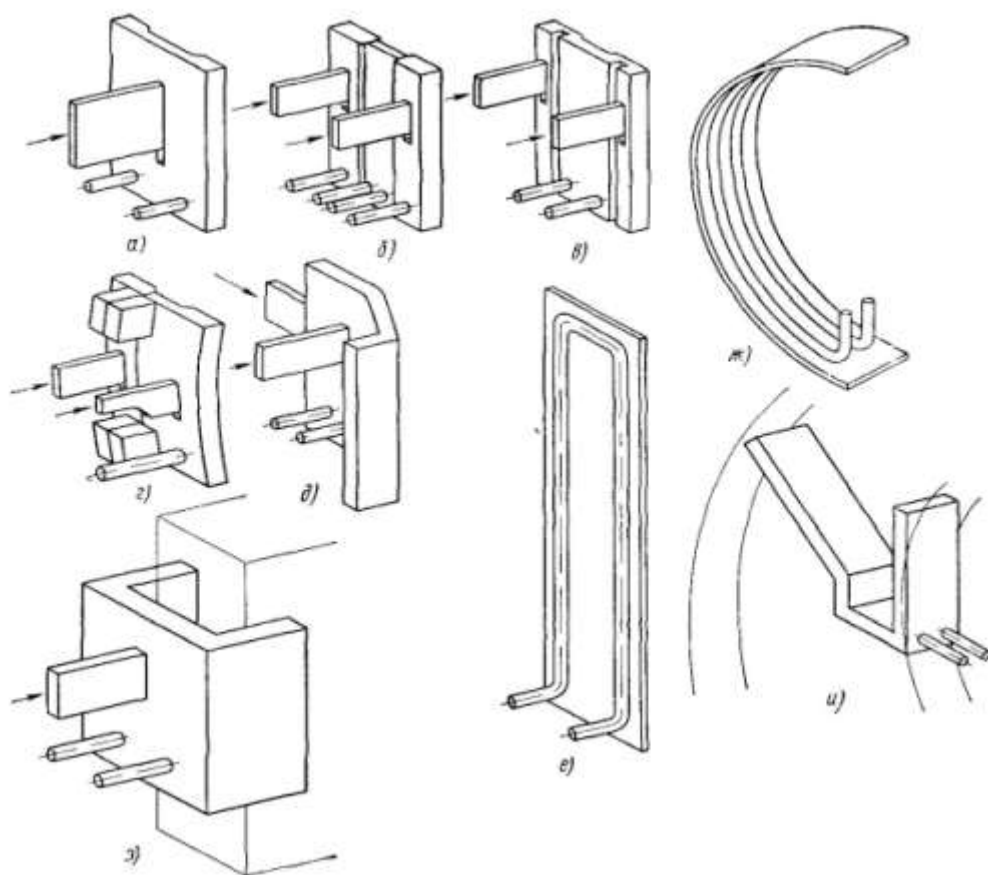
Подвижные и неподвижные формирующие устройства для электрошлаковой сварки
